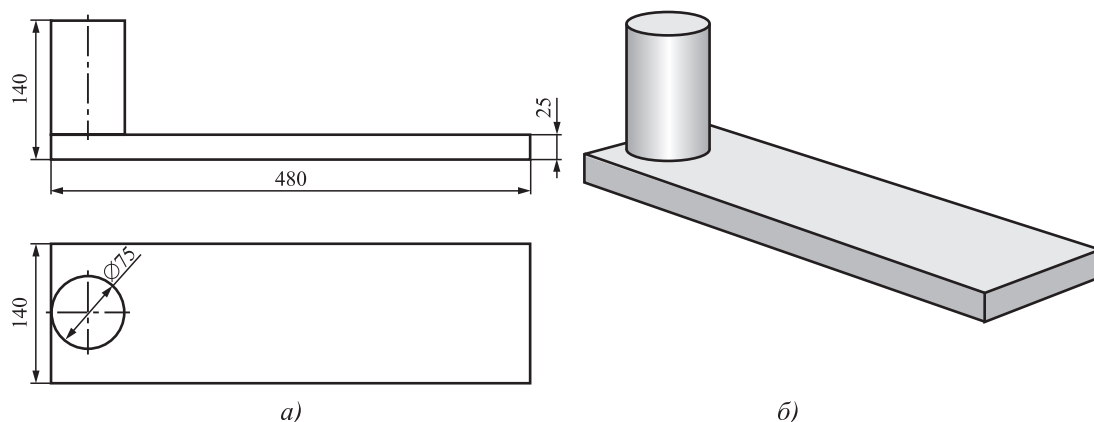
Эскиз отливки и формы (а) и 3D-модель отливки (б)
